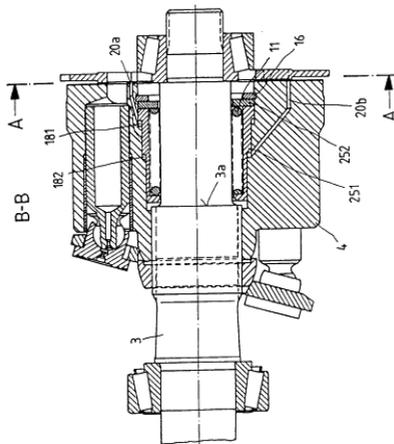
Hydraulische Zusatzanpressung Kolbentrommel-Steuerspiegel [50]
